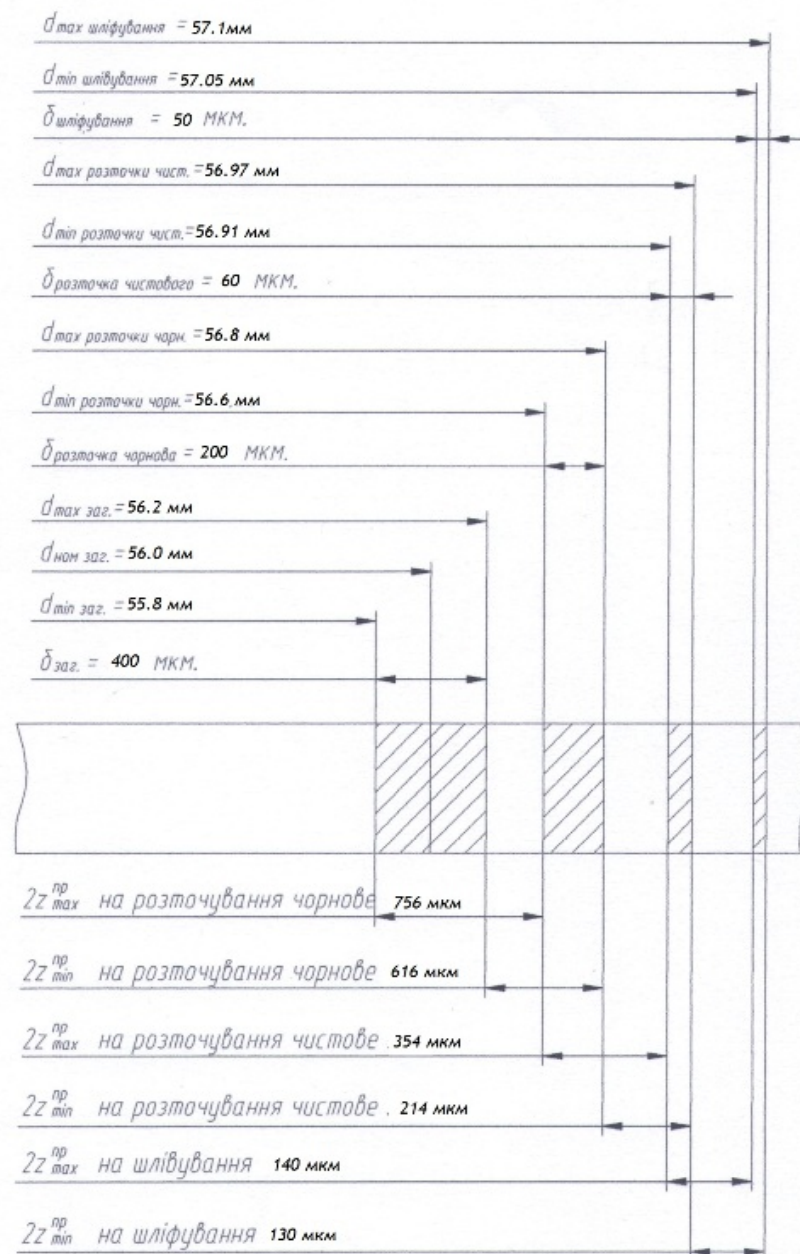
Схема розташування полів припусків і допусків на обробку
